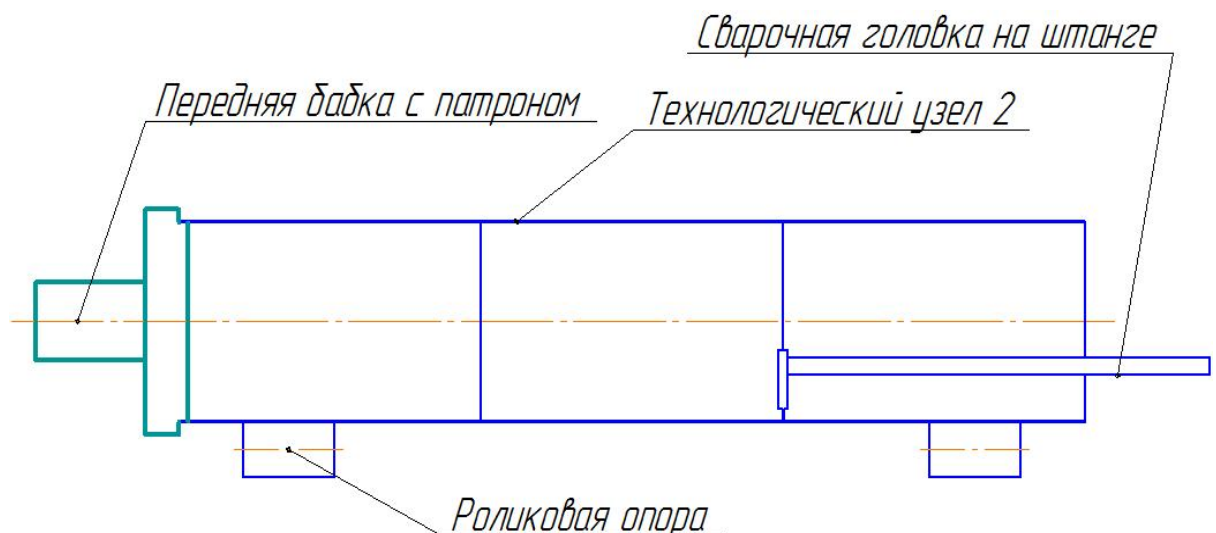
Установка технологического узла №2 для сварки изнутри третьего прохода шва №2
